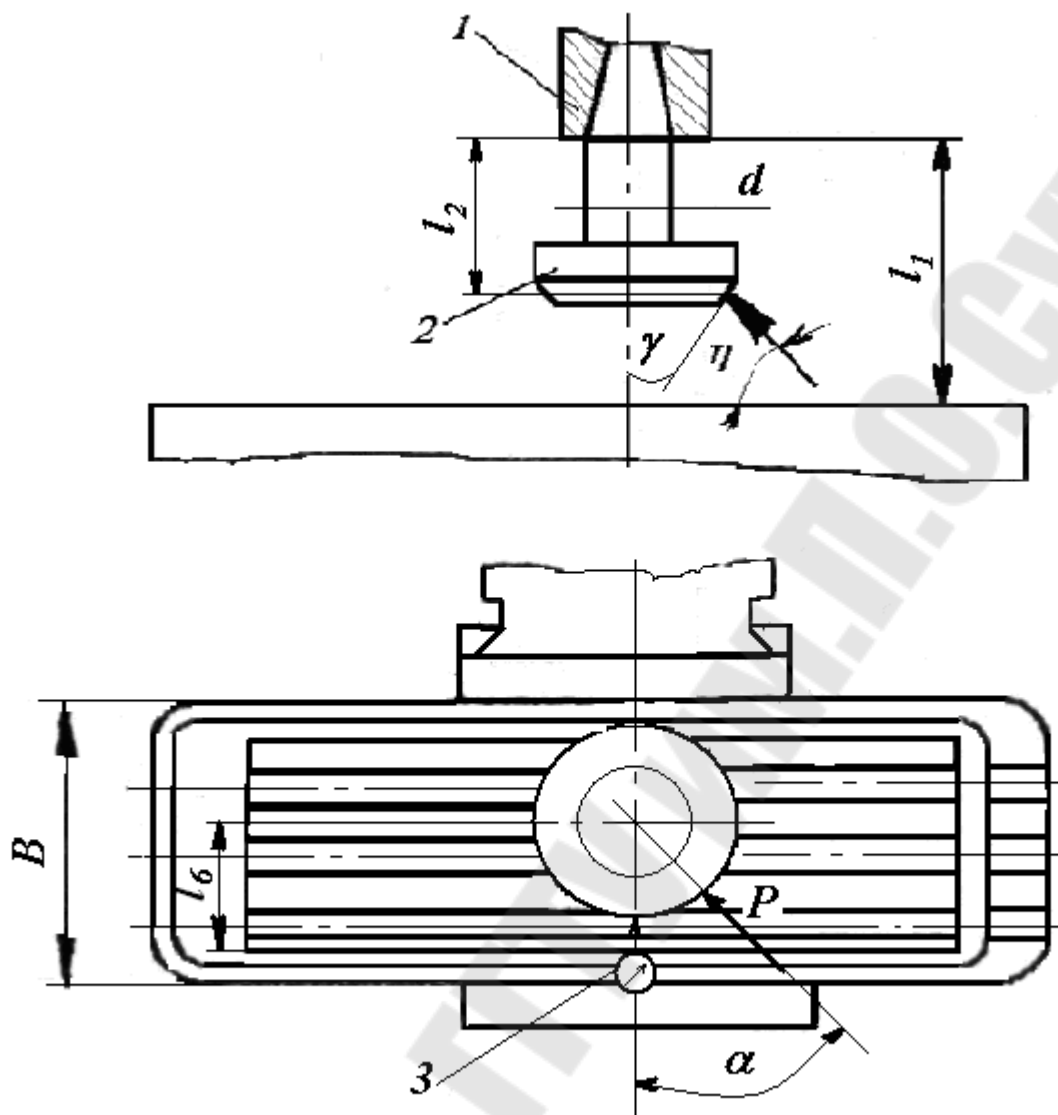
Схема измерения суммарной податливости для станка с вертикальным шпинделем
